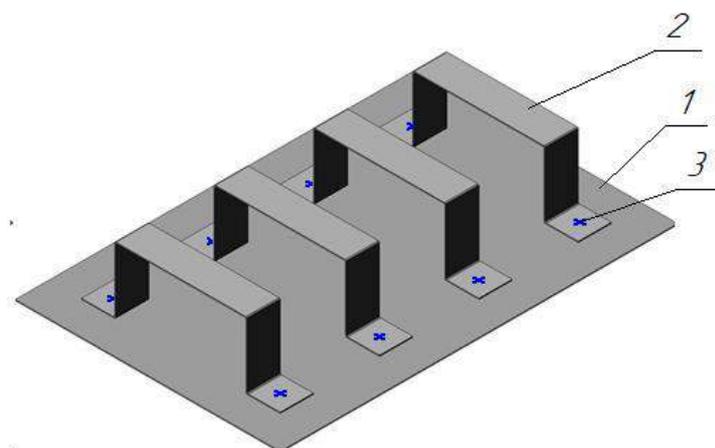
Гребенка: 1 – пластина; 2 – скоба; 3 – сварные точки
